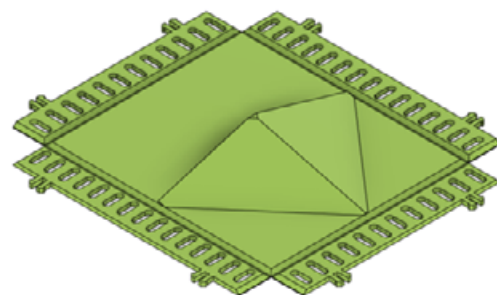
Projeto 3D do produto planificado para a fabricação.
